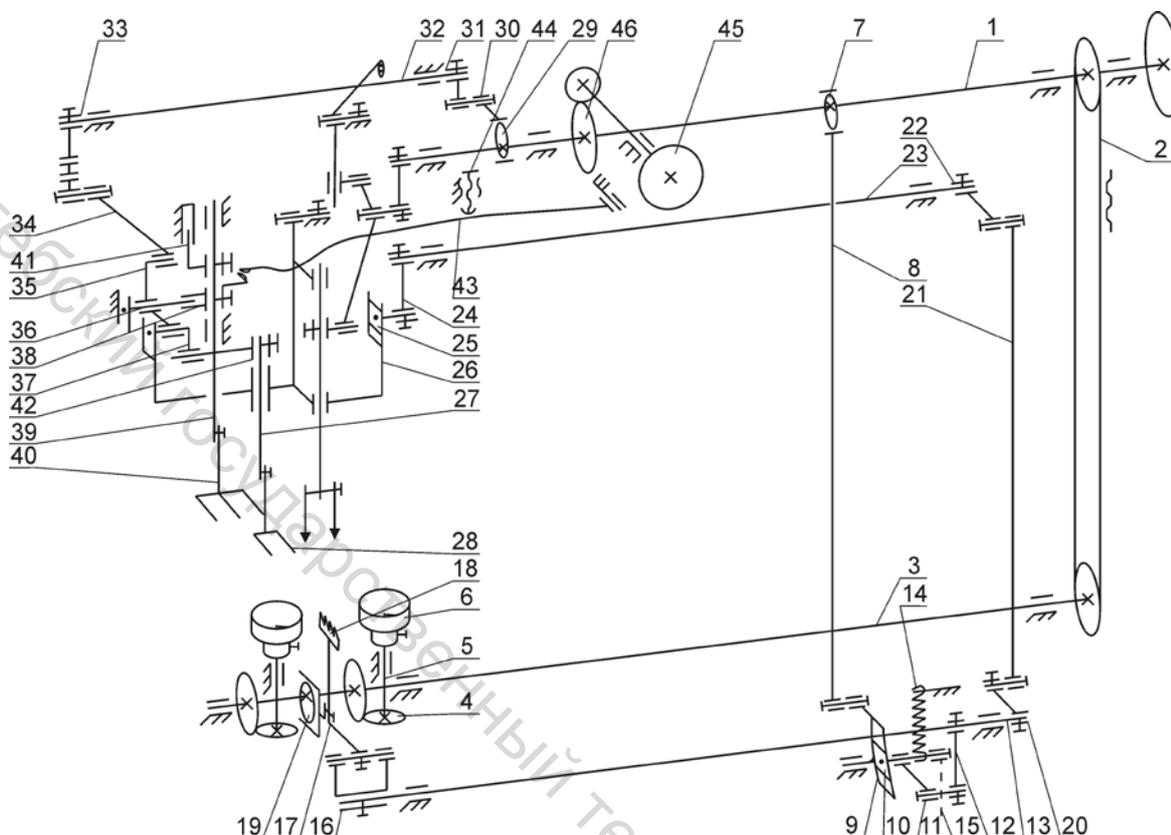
Кинематическая схема машины LG-158 Juki
